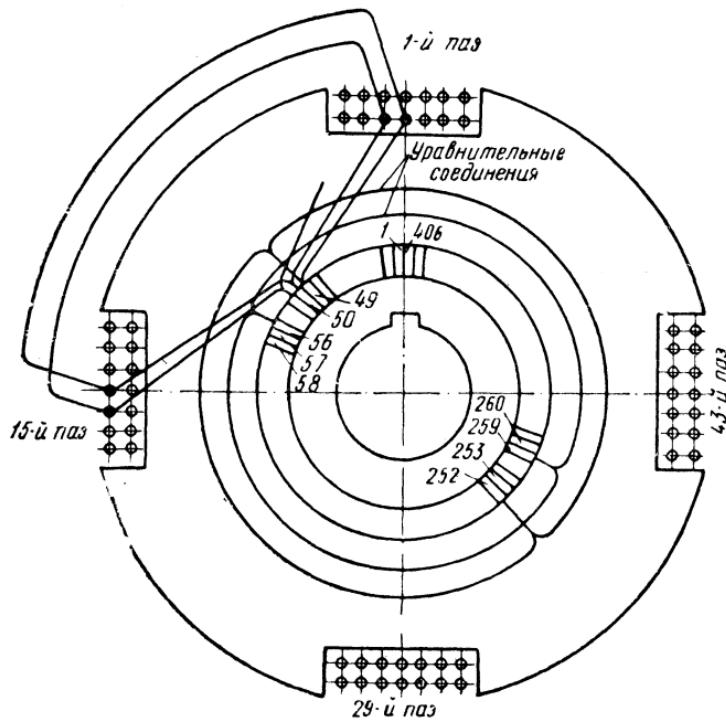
Схема соединения обмотки якоря двигателя ИБ-406 с коллекторными пластинами
